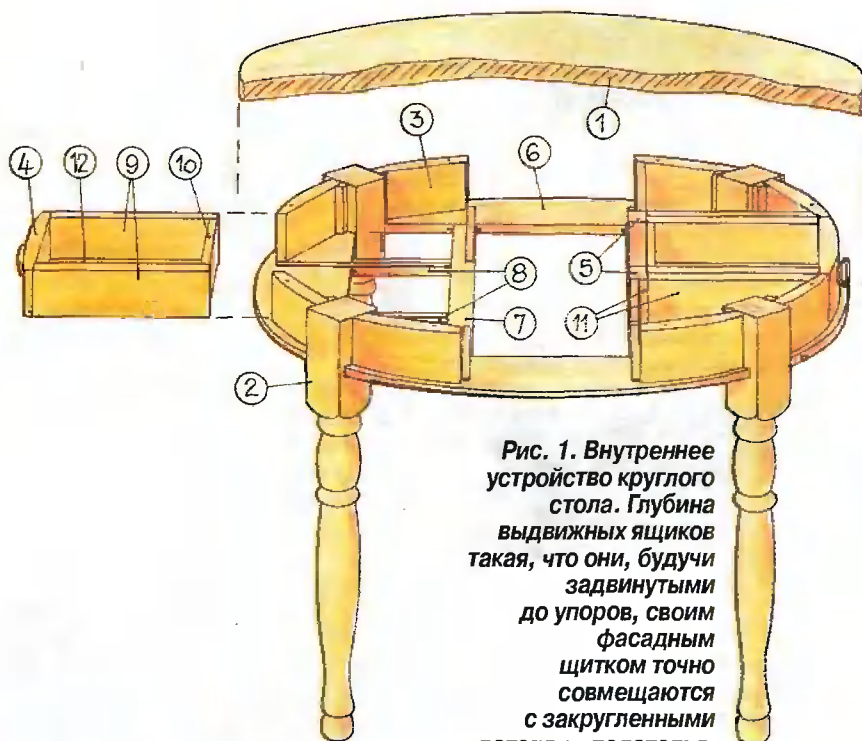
Внутреннее устройство круглого стола. Глубина выдвижных ящиков такая, что они, будучи задвинутыми до упоров, своим фасадным щитком точно совмещаются с закругленными деталями подстоля.
